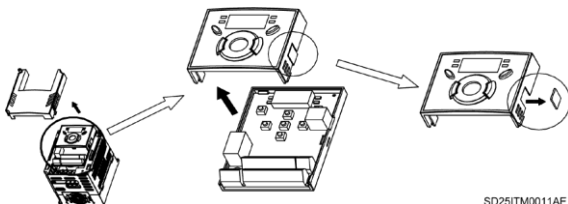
Instalação do teclado remoto / painel de operação. Passo 1
